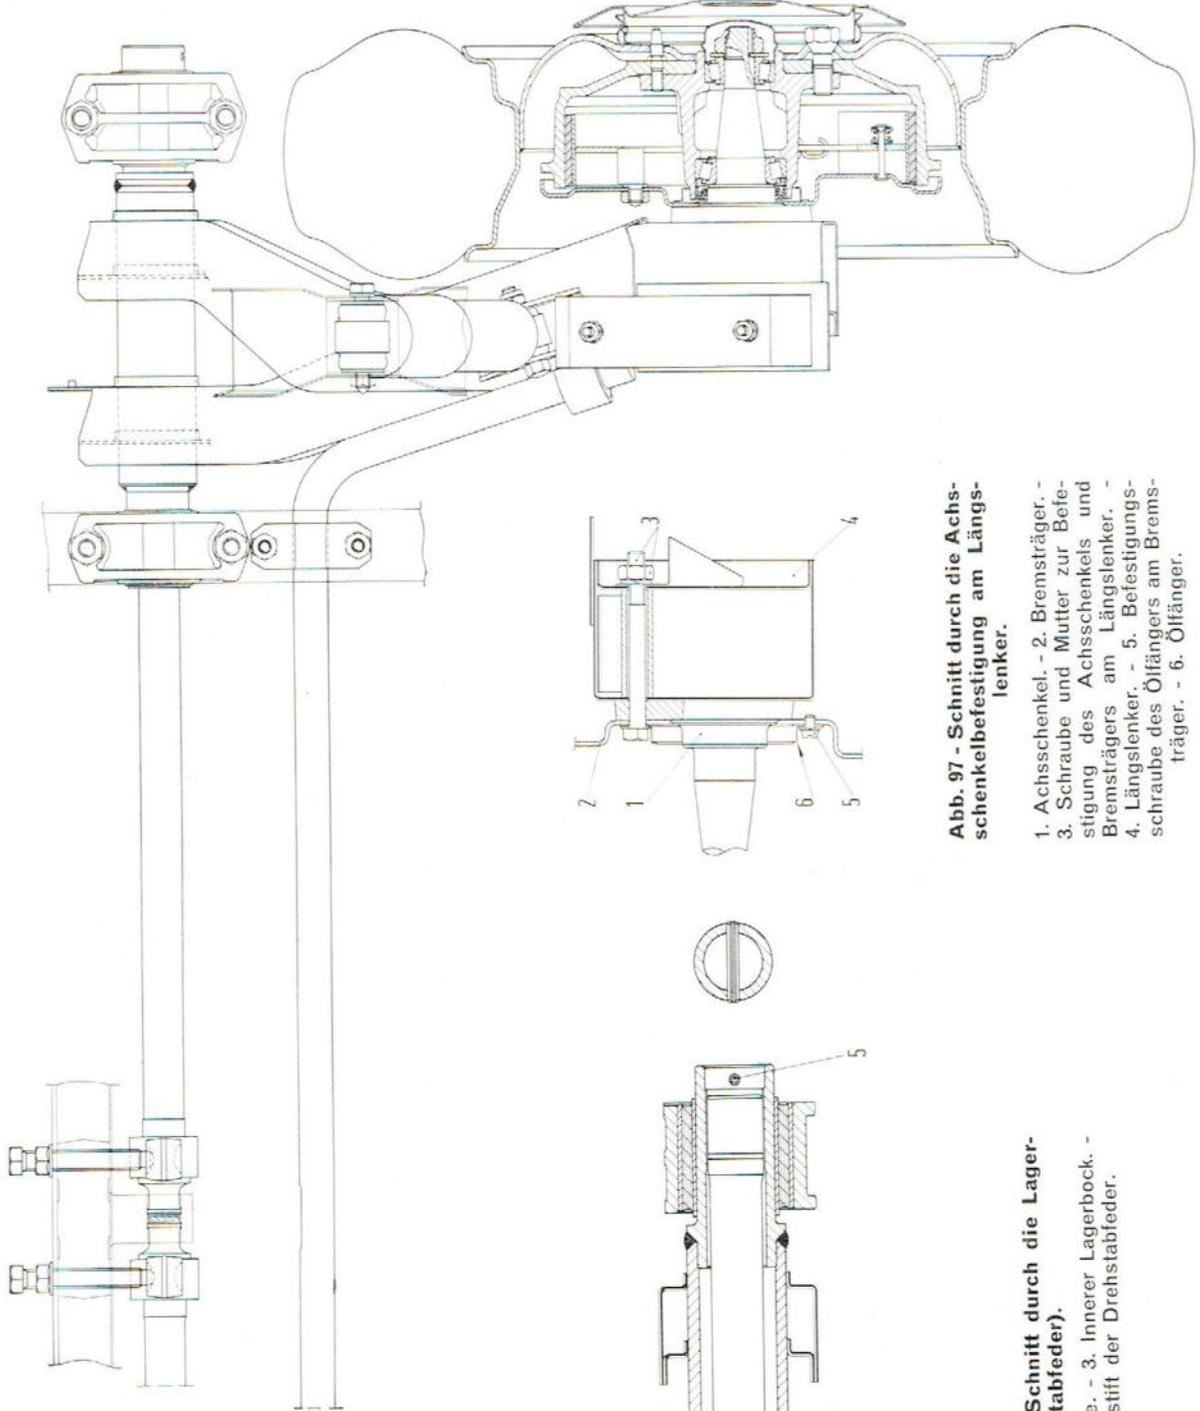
Schnittbild des rechten Hinterrads und seiner Aufhängung.
